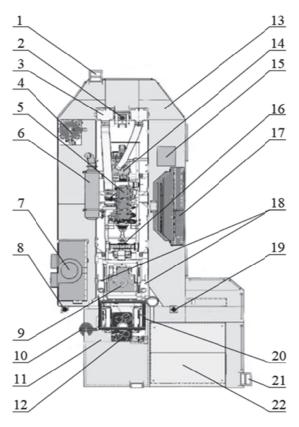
Устройство буровой установки: 1 – стремянка обслуживания буровой установки; 2 – домкрат; 3 – очиститель воздуха; 4 – приемный резервуар; 5 – двигатель; 6 – глушитель; 7 – сборник пыли (или напольный бак воды, если установлен); 8 – домкрат; 9 – гидравлический бак; 10 – карусельный магазин; 11 – платформа буровой установки; 12 – вращающаяся головка; 13 – задняя платформа; 14 – компрессор A/C; 15 – бак смазочного масла скважинного забойного бура; 16 – привод насоса; 17 – охладитель; 18 – цилиндры подъема вышки; 19 – домкрат; 20 – вышка; 21 – стремянка обслуживания буровой установки; 22 – кабина
